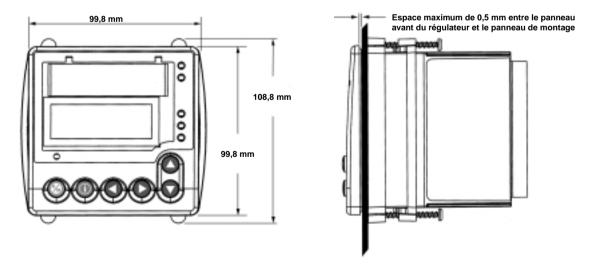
Dimensions, vue de face et dimension de l'écart du joint.
